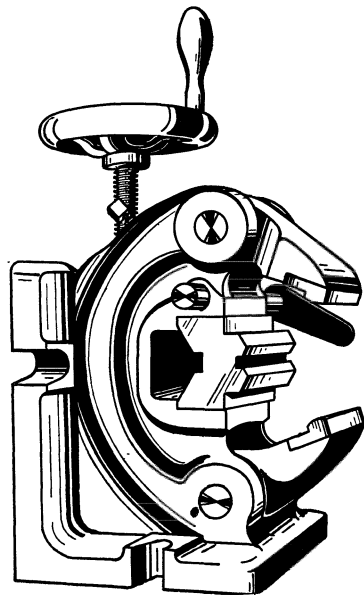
Zentrisch spannender Maschinenschraubstock.
